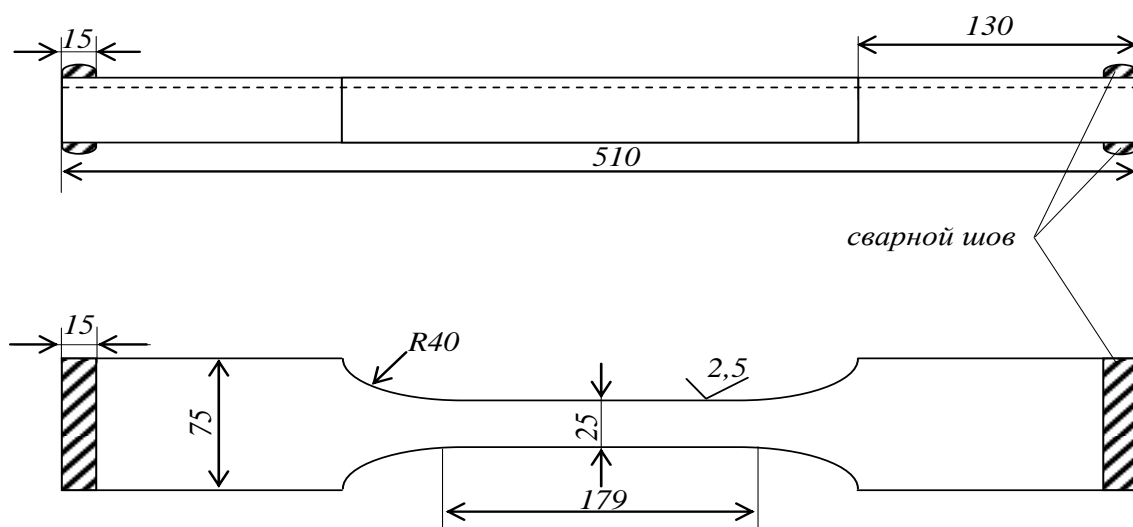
Образец плакированной стали для испытаний на растяжение
